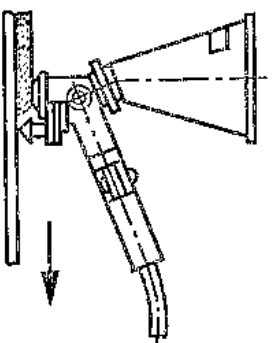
Схема полуавтоматической сварки под флюсом стыковых швов
